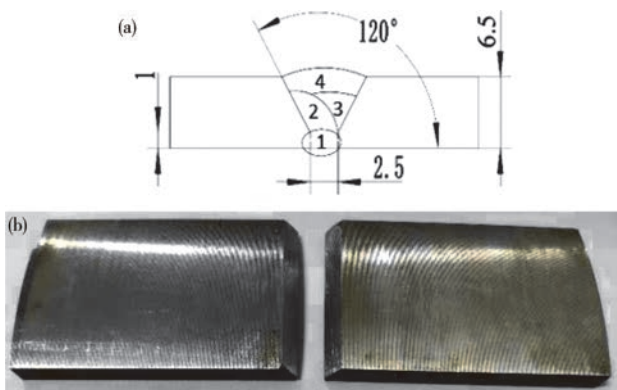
T-TIG-01 焊接试样坡口形式: (a) 坡口几何尺寸(单位: mm); (b) 坡口实物图
